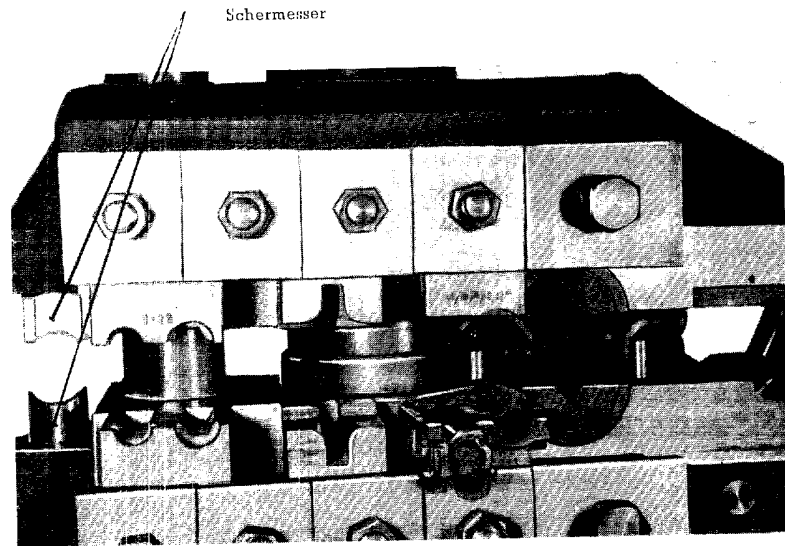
Vorderansicht des gehobenen Maschinenkopfes mit eingebauten Matrizen und Gesenke
